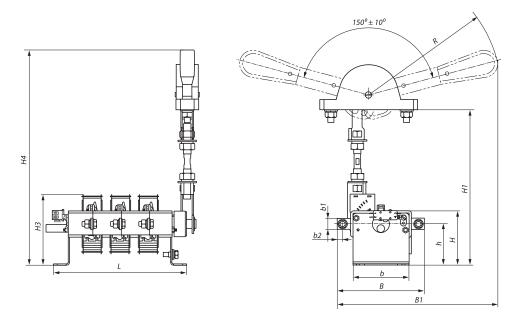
Выключатель-разъединитель универсальный трехполюсный на одно направление с д/г камерами, передняя смещенная несъемная левая/правая рукоятка
